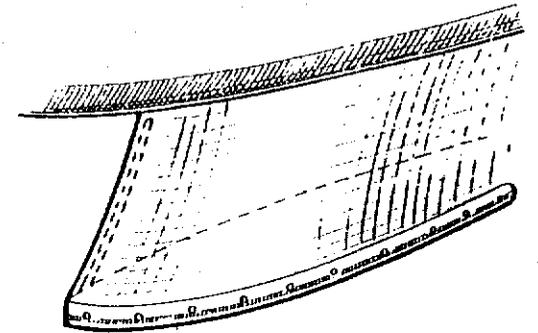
Raccordement des toiles à l'arrière du patin.
